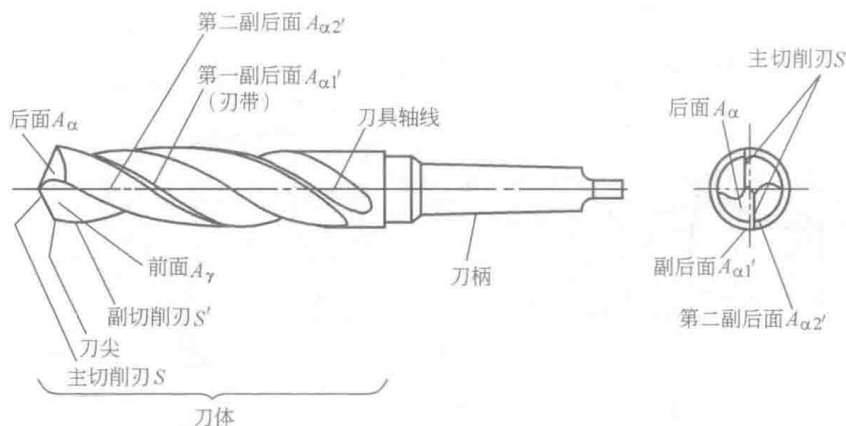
麻花钻切削部分上的切削刃和刀具表面
